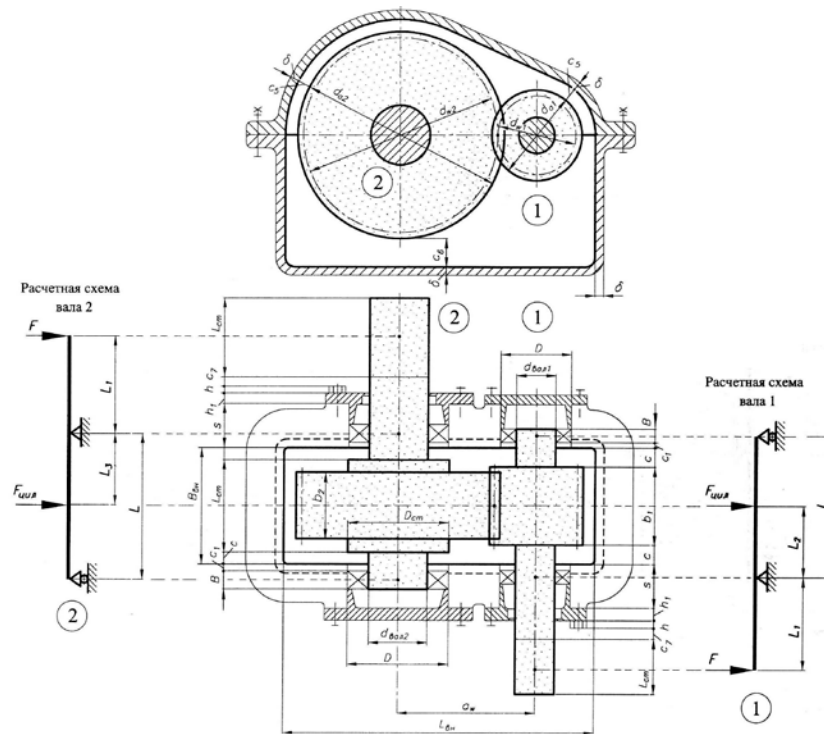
Схема компоновки одноступенчатого цилиндрического редуктора
